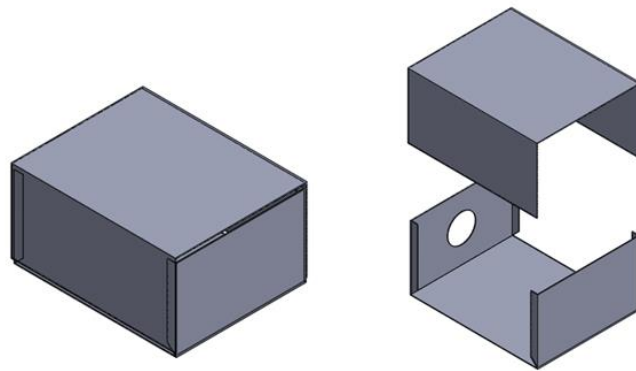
Caja contenedora de los polvos finos desarrollada en el módulo Sheetmetal ensamblada y vista explosionada.
